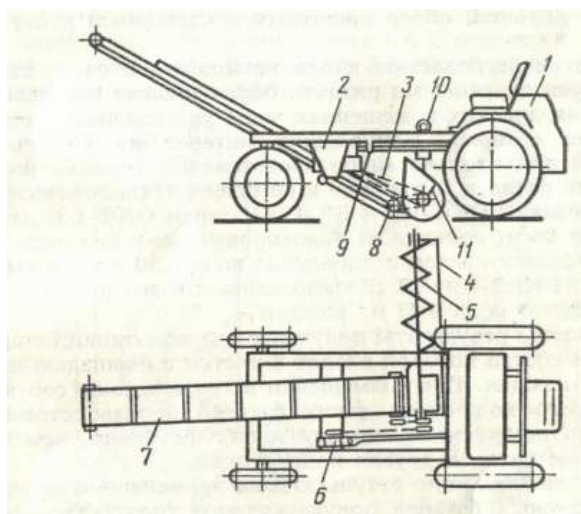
Схема навозоуборочной машины НУМЗ-3: 1 – самоходное шасси Т-16 М; 2 – рама с подвеской; 3 – цепь привода шнека; 4 – кожух шнека; 5 – шнек; 6 – редуктор; 7 – цепочно-скребковый транспортер; 8 – цепь привода транспортера; 9 – карданный вал; 10 – гидроцилиндр; 11 – лопасть швырялки
